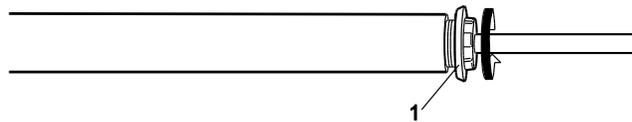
Desserrer la vis placée sur la flasque mobile
